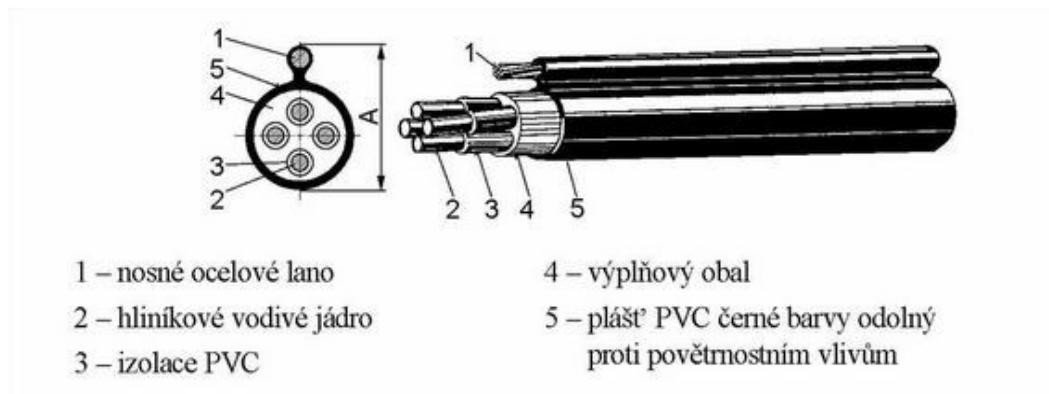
Konstrukční provedení odbočky k odběrnému místu, převzato z [5]
